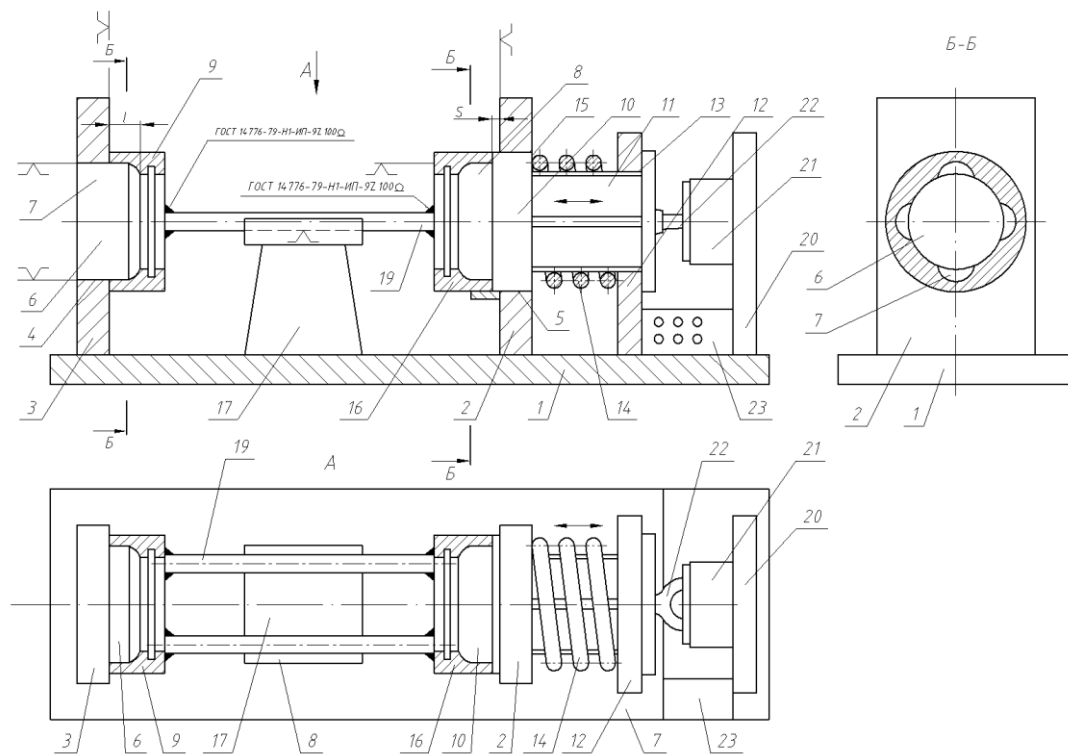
Пристрій для зварювання секцій гіперболічного шнека.
